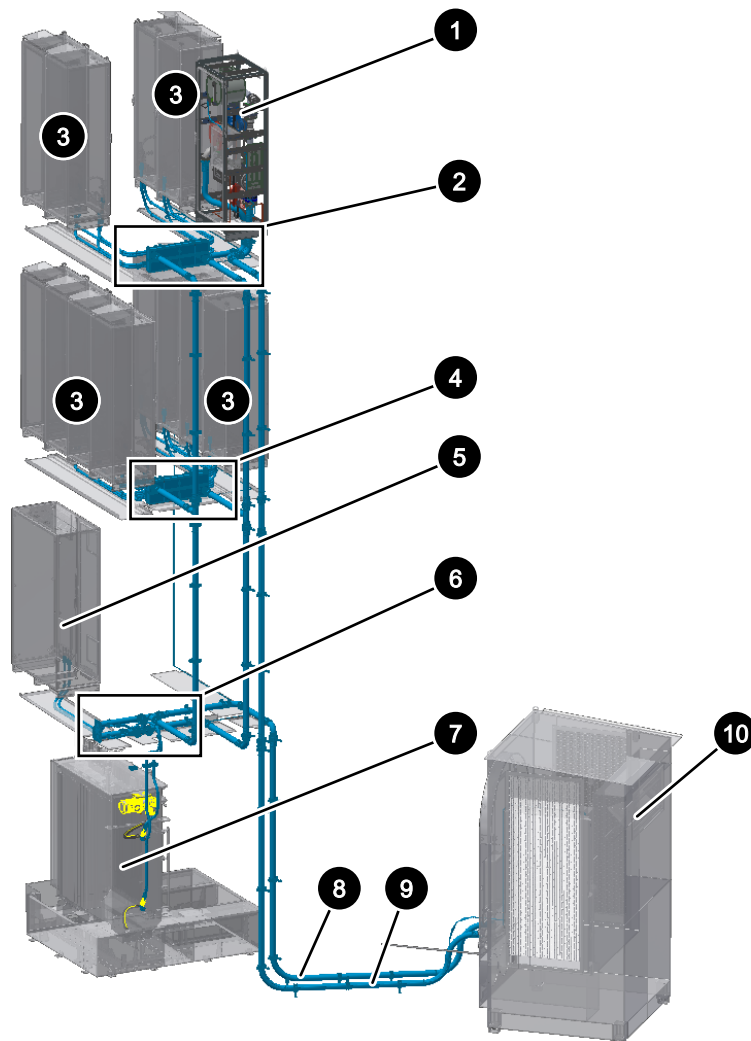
Gesamtansicht des Kühlsystems mit Rückkühler
